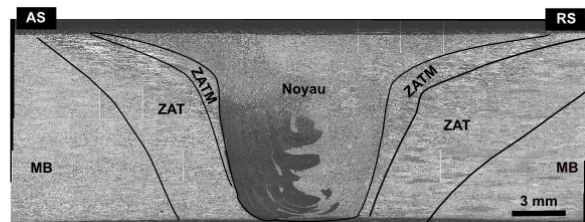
Macrostructure des joints soudés par FSW en alliages d'aluminium
